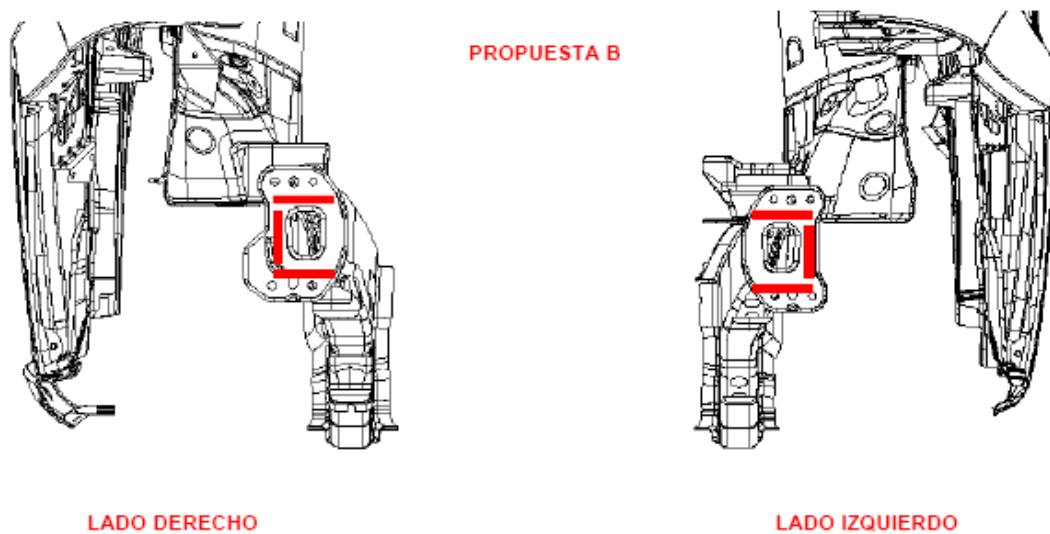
Propuesta B soldadura de tapetas
